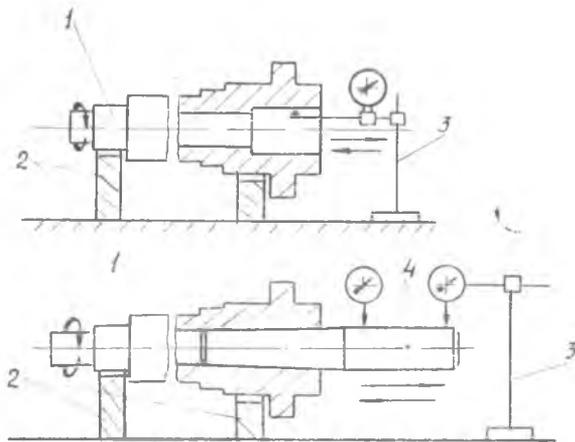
Схемы проверки соосности цилиндрических поверхностей: *1* — проверяемая деталь; *2* — призма; *3* — стойка индикаторная; *4* — оправка
